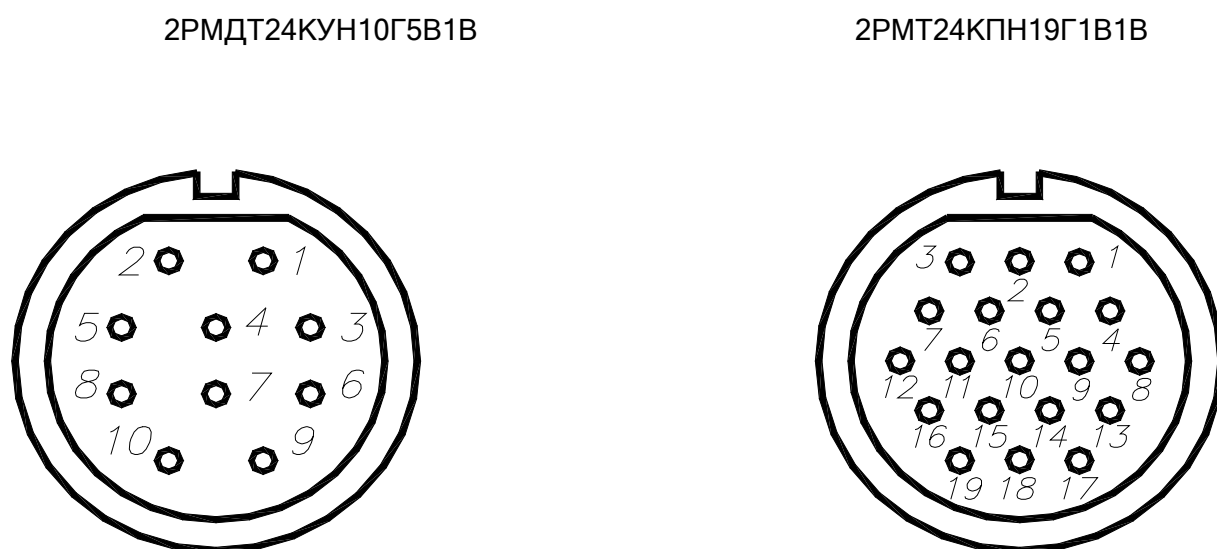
Нумерация контактов соединителей со стороны пайки
